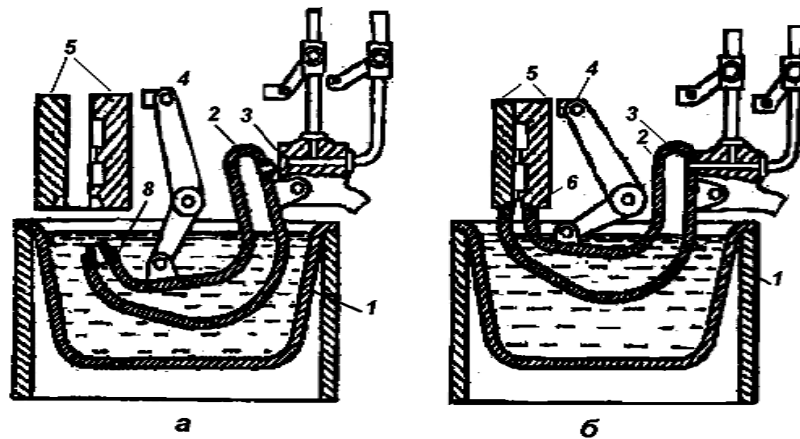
Схема будови і роботи компресорної машини з гузнеком: а-положення коли метал заповнює гузнек; б-положення коли метал витискається в металеву пресформу.
